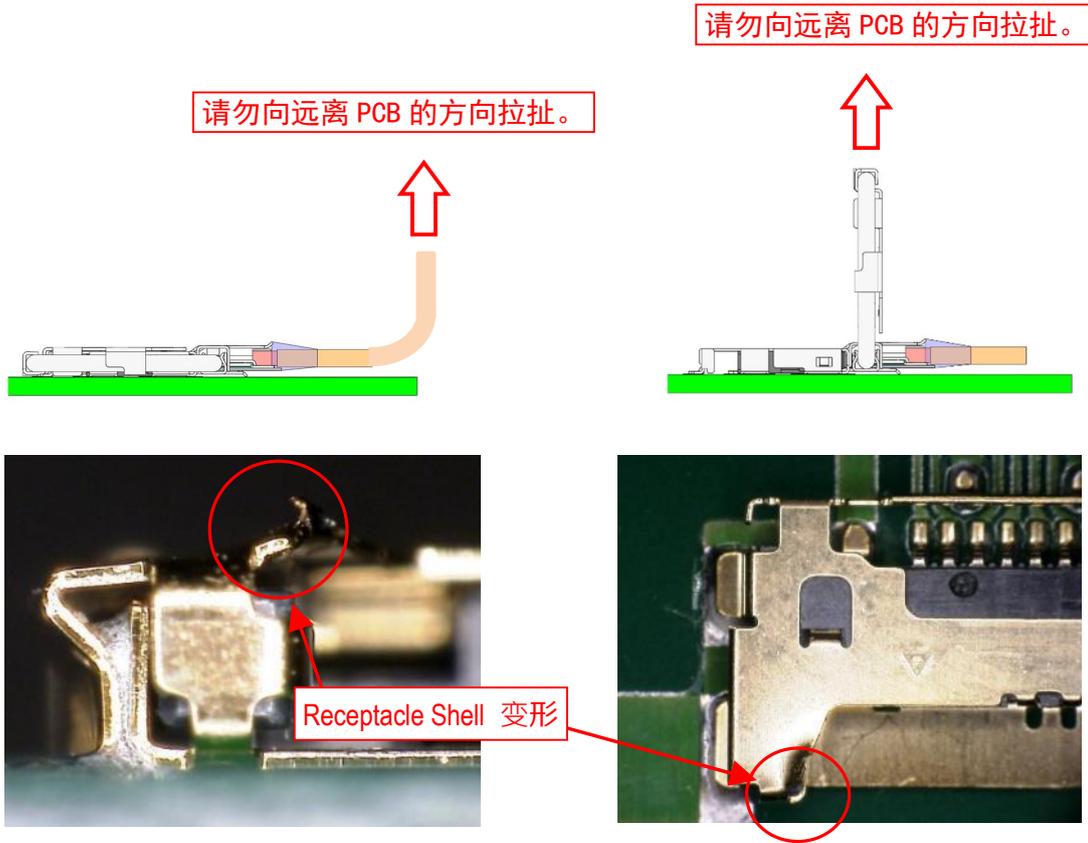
Harness 与 Lock Bar Assembly 错误操作示范
